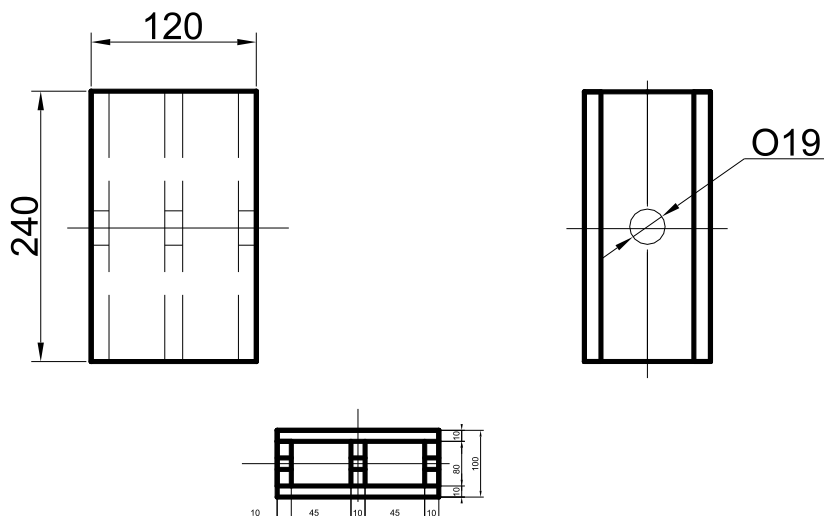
Сварной вкладыш промежуточного узла верхнего пояса
